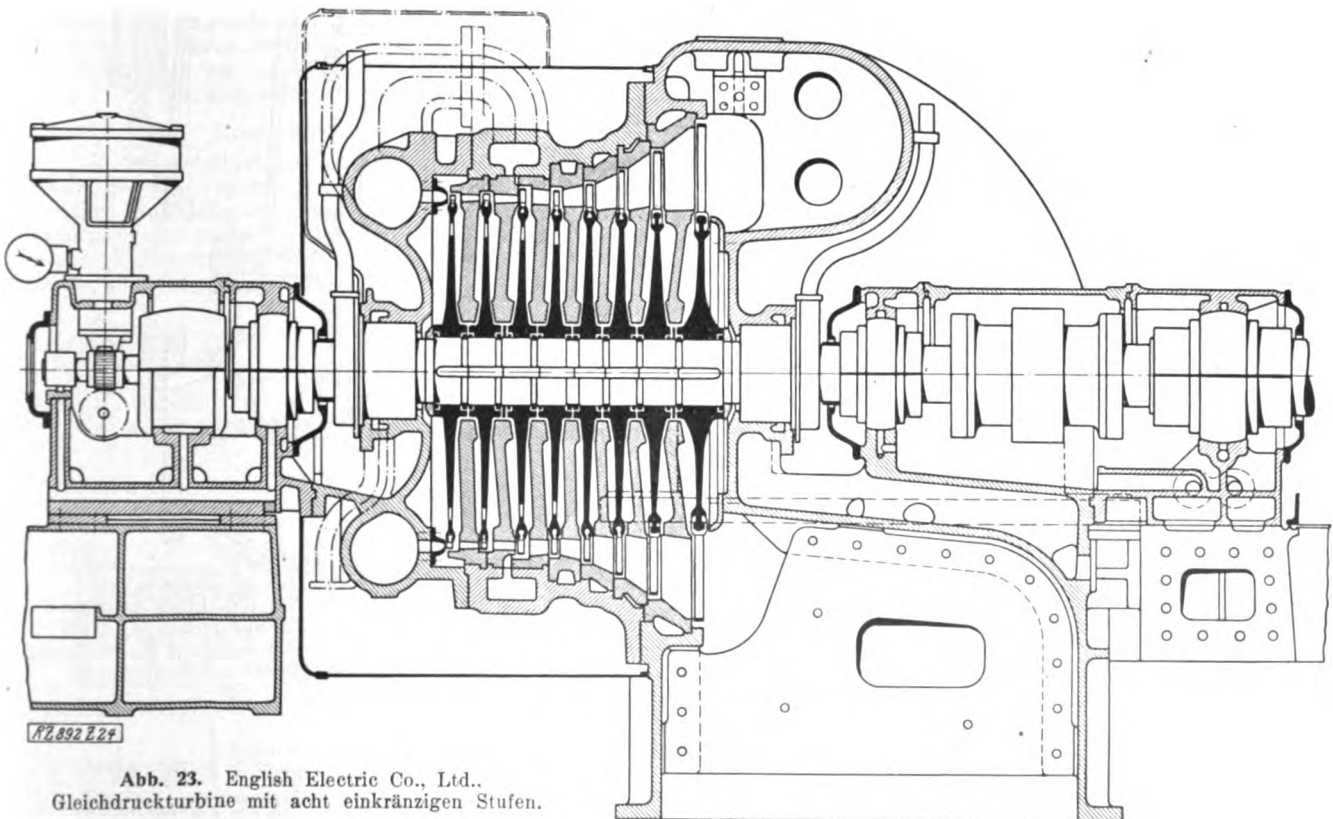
English Electric Co., Ltd., Gleichdruckturbine mit acht einkränzigen Stufen.
